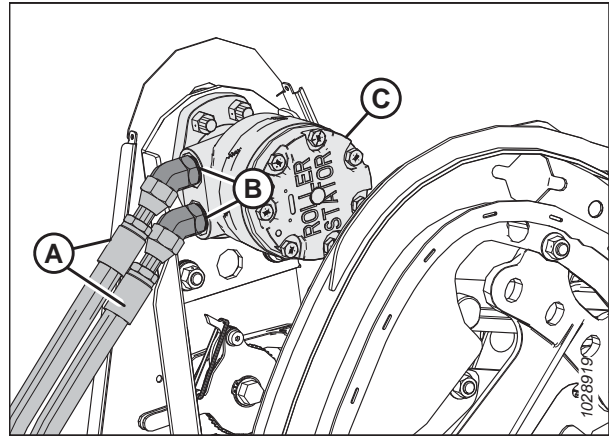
Haspelmotor und Hydraulikschläuche
